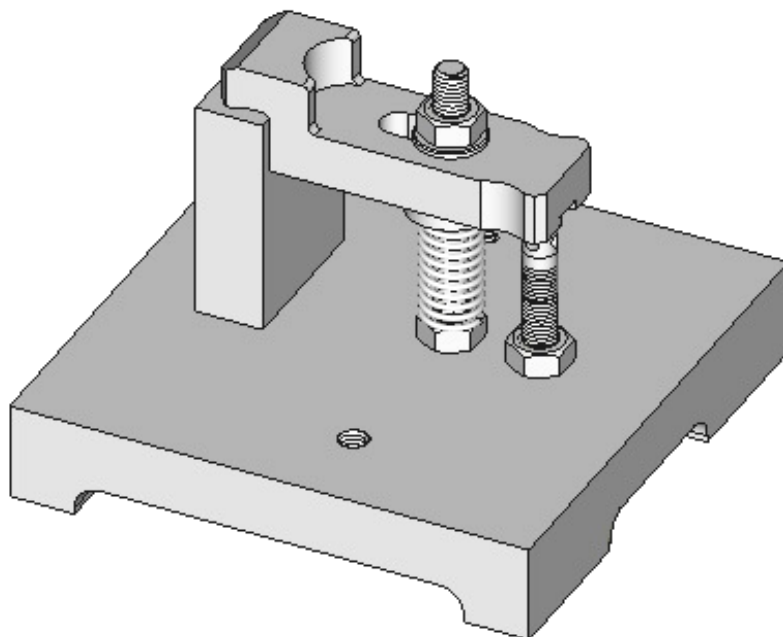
Прихват ступенчатый в приспособлении с заготовкой
